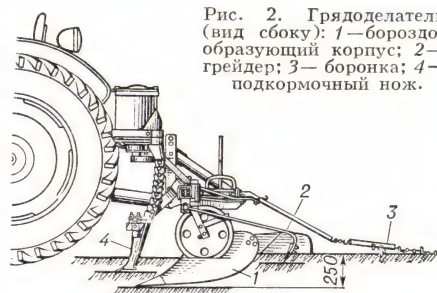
Грядоделатель (вид сбоку): 1—бороздообразующий корпус; 2—грейдер; 3—боронка; 4—подкормочный нож.
